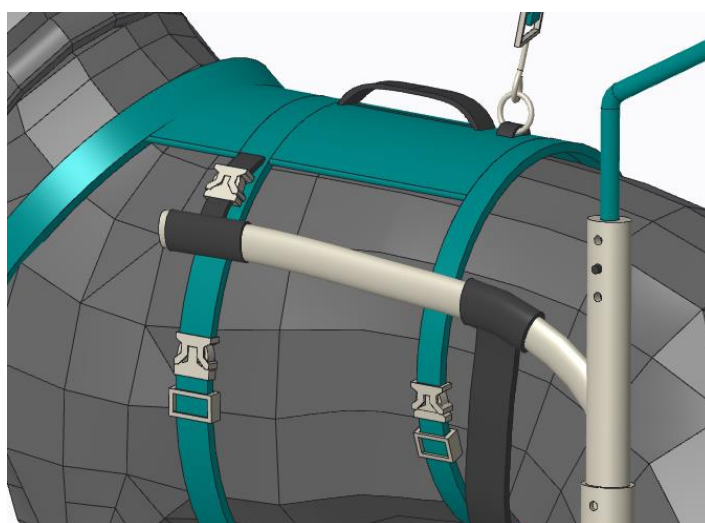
Kopča na konstrukciji i sistem za podešavanje dimenzija
